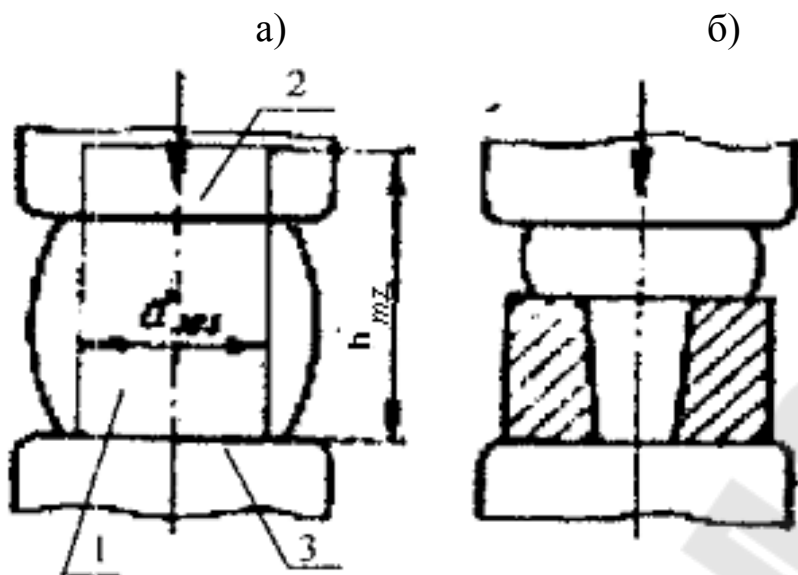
Схема операции ковки: а-осадка б-высадка
